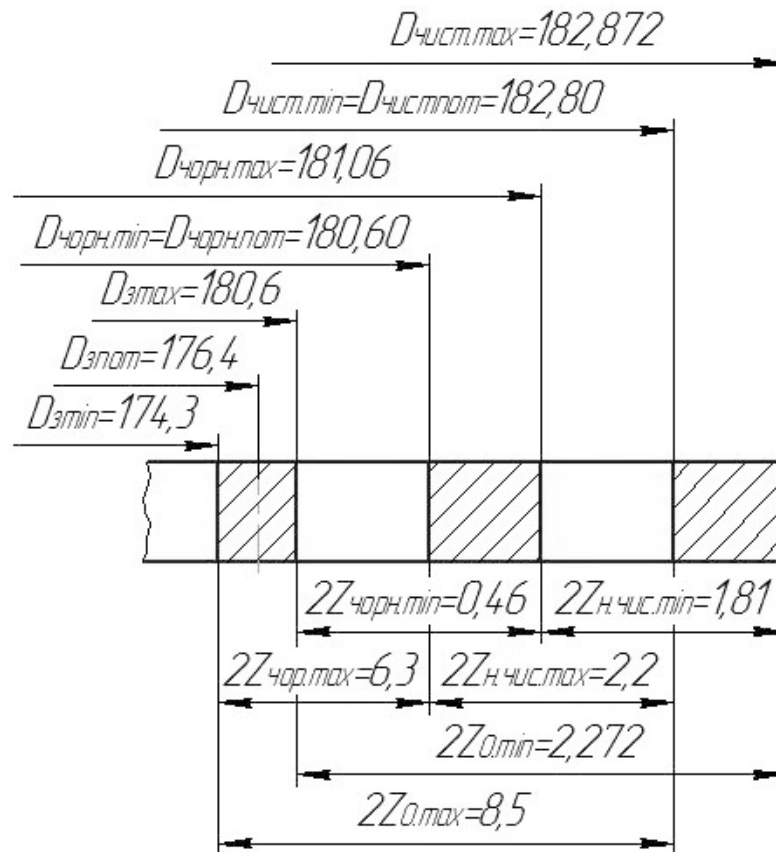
Розташування полів допусків і припусків на обробку внутрішньої поверхні $\varnothing 184H8^{(+0,072)}$
